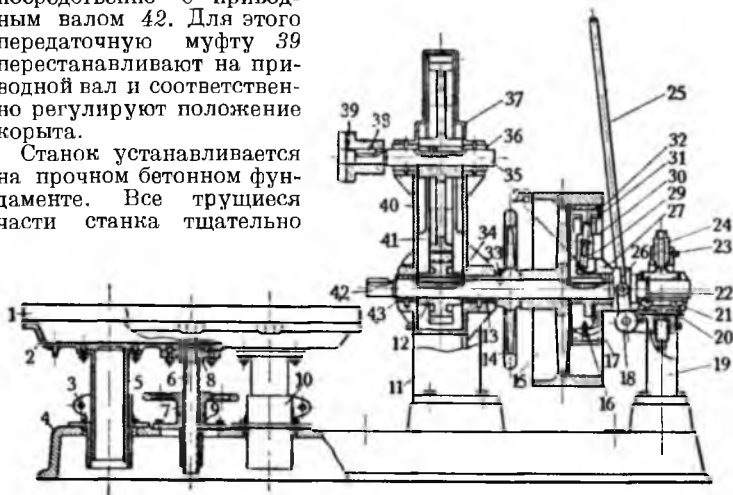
Станок для прижигания и приработки моторных подшипников:
